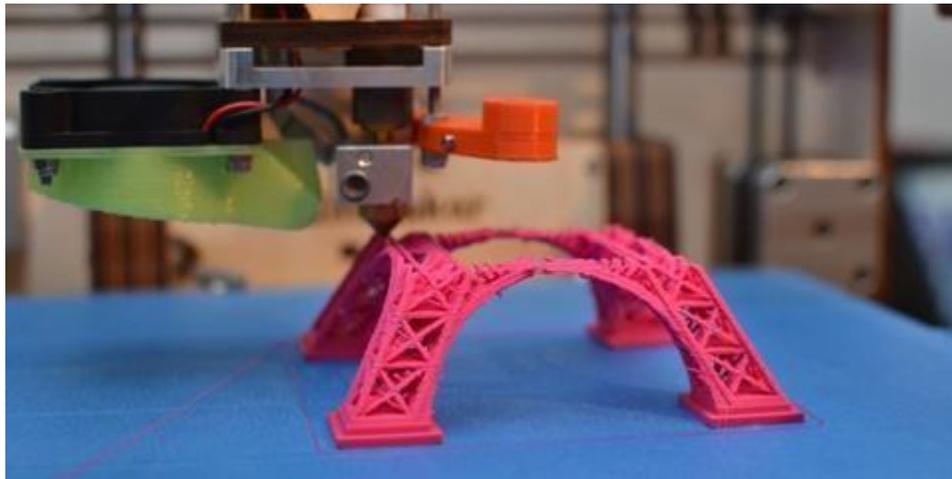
Impresión 3D por deposición de material fundido (FDM) [21].
